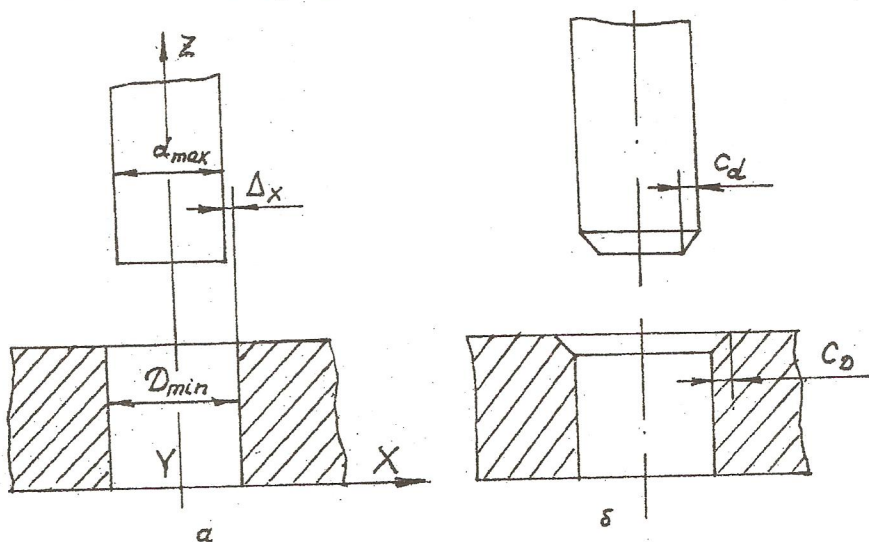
Схема сборки деталей, сопрягаемых по цилиндрическим поверхностям: а - детали без фасок; б - детали с фасками
